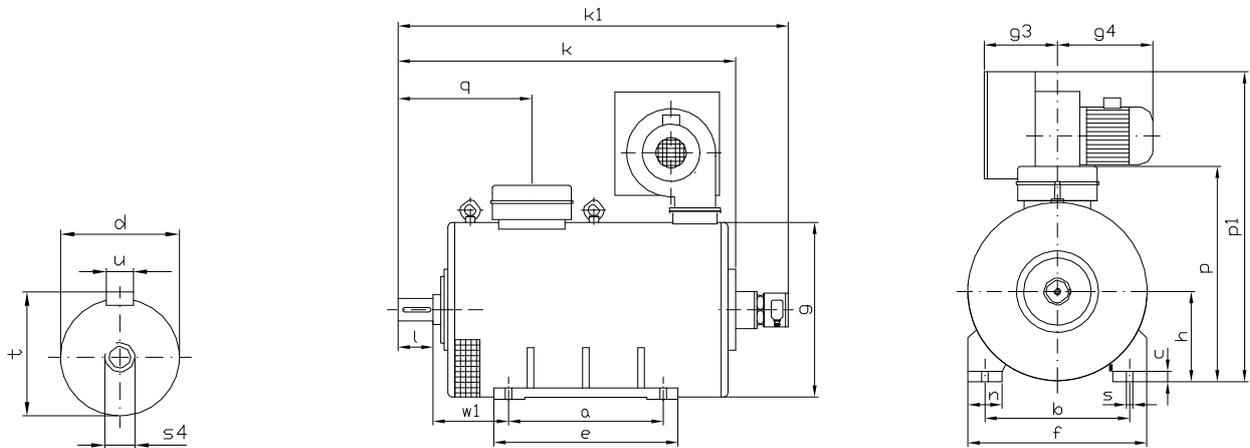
Drehstrom-Käfigläufermotor mit Encoder mit Anbauflansch: Kühlung IC 06, Schutzart: IP 23, Bauform: IM B3
